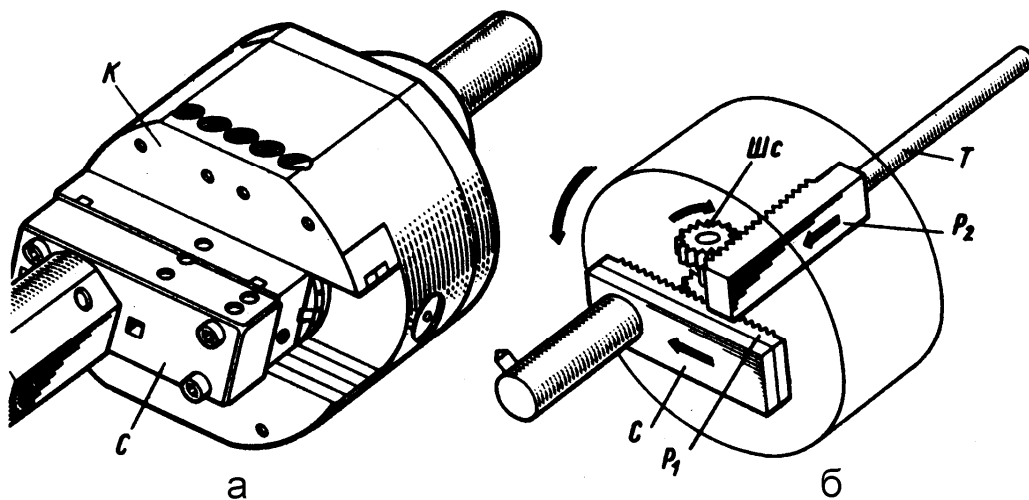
Плансупортна головка: а – загальний вигляд; б – побудова
